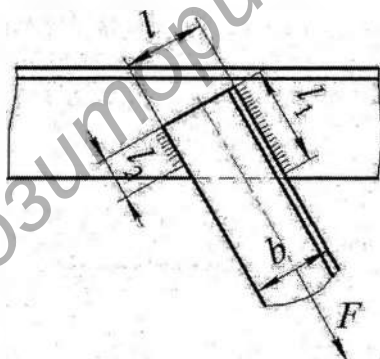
Схема сварного соединения [3, с. 35]
